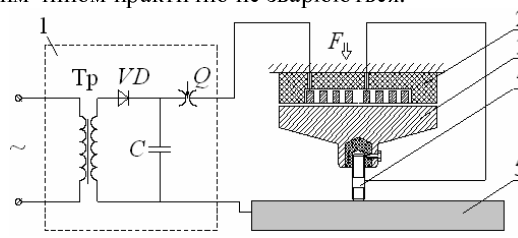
Принципова схема ударно-конденсаторного зварювання з магнітно-імпульсним приводом: 1 – генератор імпульсних струмів; 2 – дисковий індуктор; 3 – штовхач; 4 – зварювана деталь; 5 – корпусна деталь; F – зусилля притискування деталей
